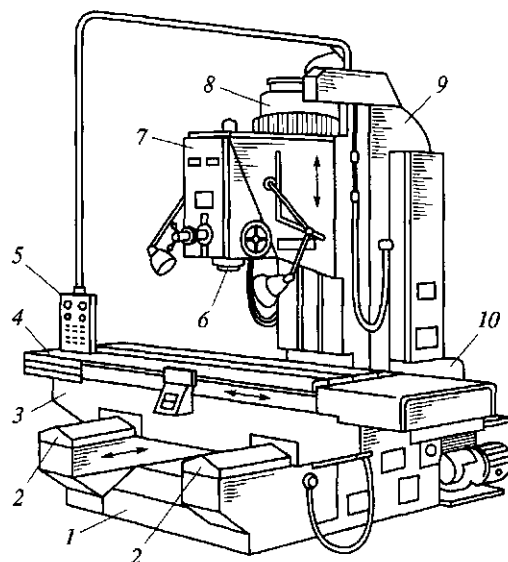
Бесконсольный вертикально-фрезерный станок:
